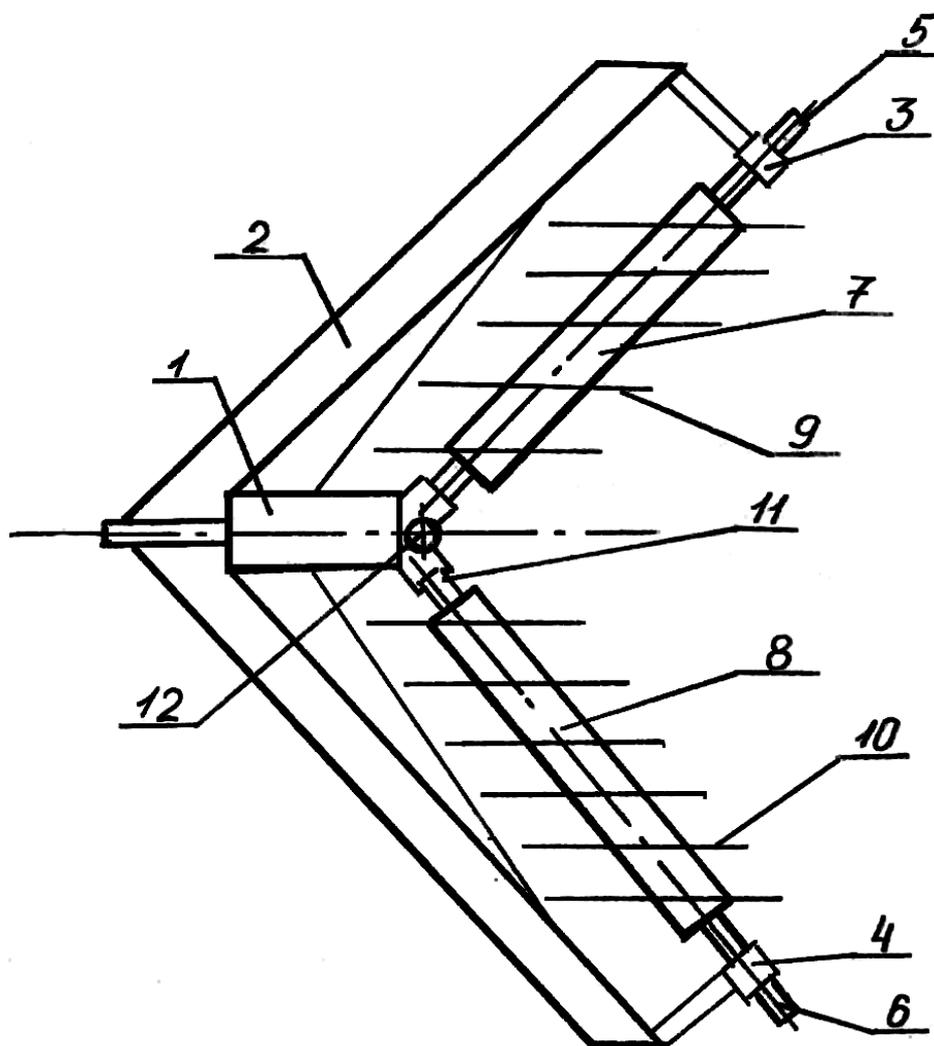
Почвообрабатывающий рабочий орган, вид сверху
